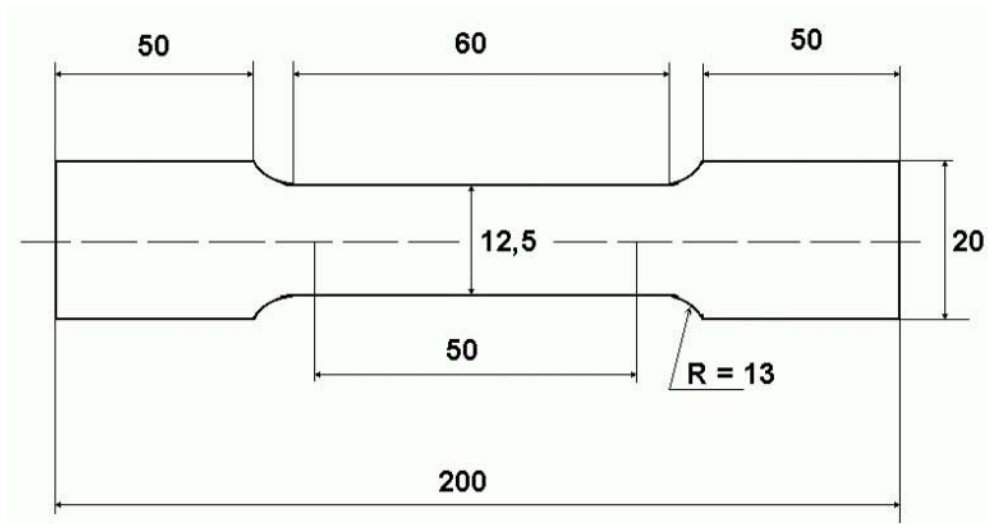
Dimensão do corpo-de-prova de tração utilizado
